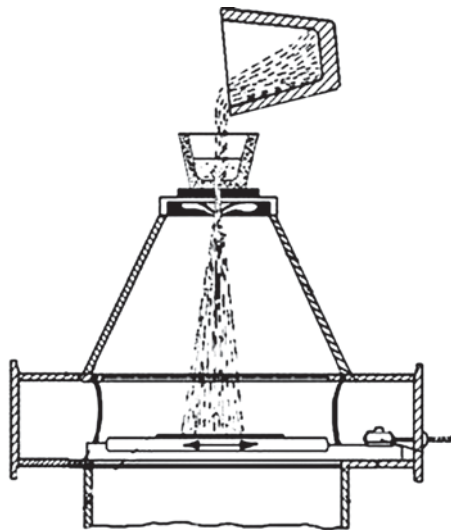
Установка розпилення розплаву з кристалізатором для отримання заготовок методом струменевого формування
